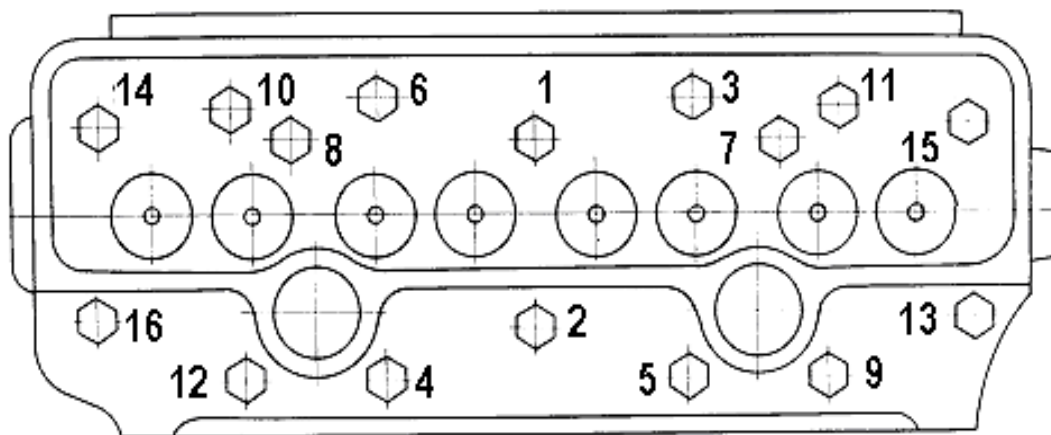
Схема последовательности затяжки болтов крепления головки цилиндров
